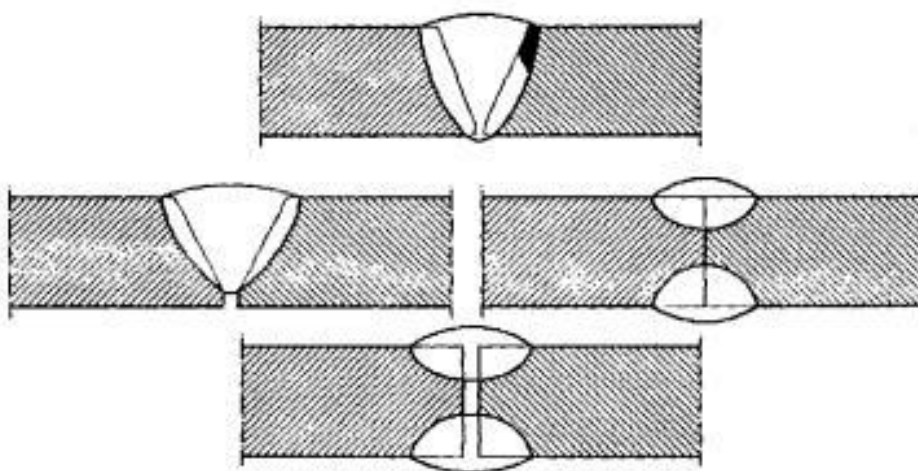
Виды непроваров в сварных соединениях.
